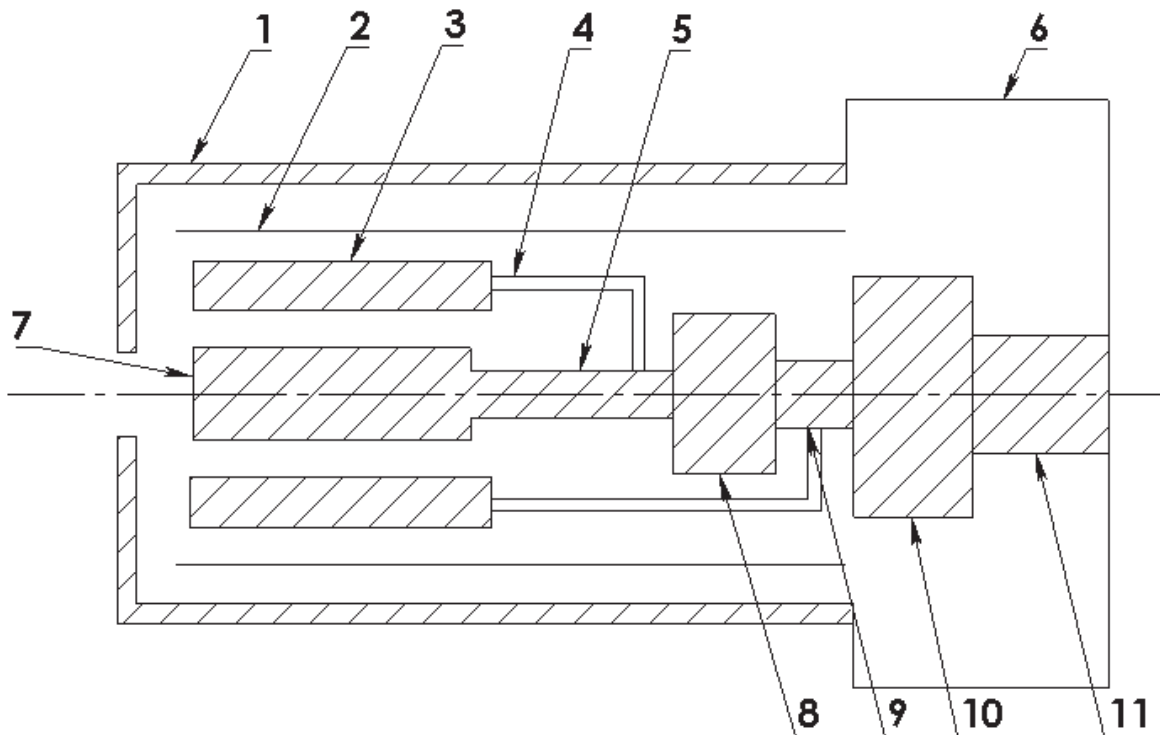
Схема конструкции катода с бариевым эмиттером: 1 — пусковой электрод; 2 — тепловые экраны; 3 — нагреватель; 4 — штанги; 5 — проставка; 6 — корпус; 7 — капсула с эмиттером; 8 — токоподвод К; 9 — токоподвод Н; 10 — изолятор; 11 — магистраль подачи рабочего тела
